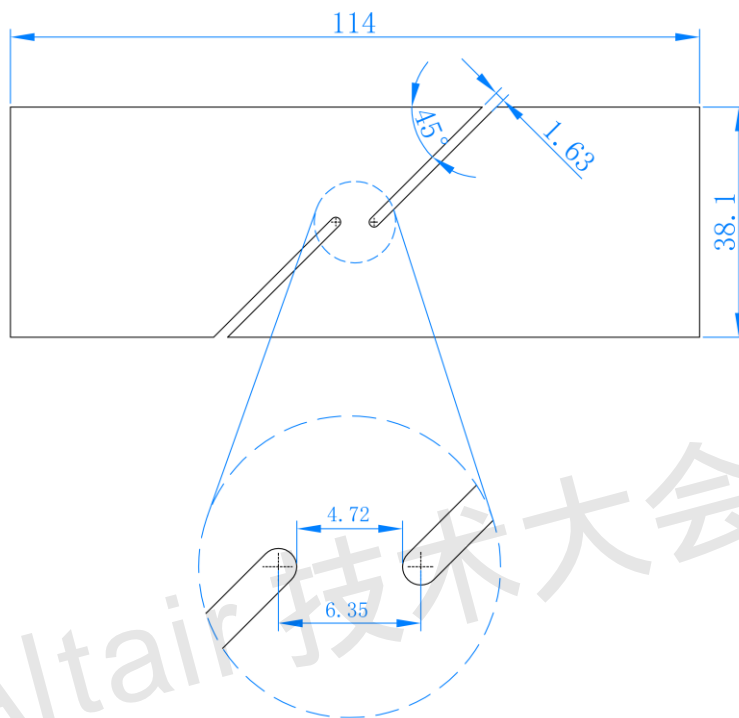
ASTM B831 标准中薄板纯剪切试验试样尺寸 (mm)
